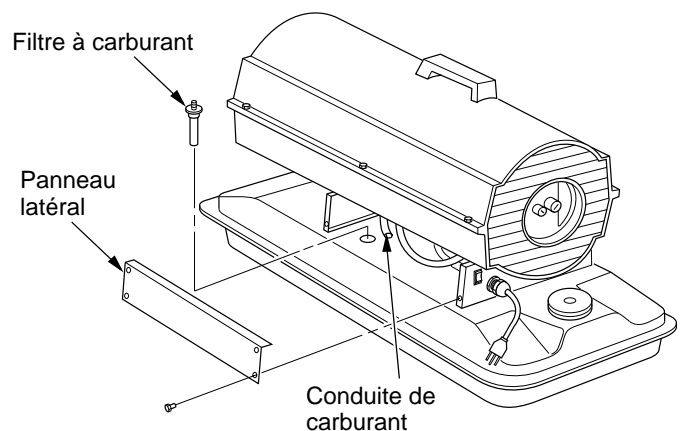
Dépose du filtre à carburant, Modèle GK20
